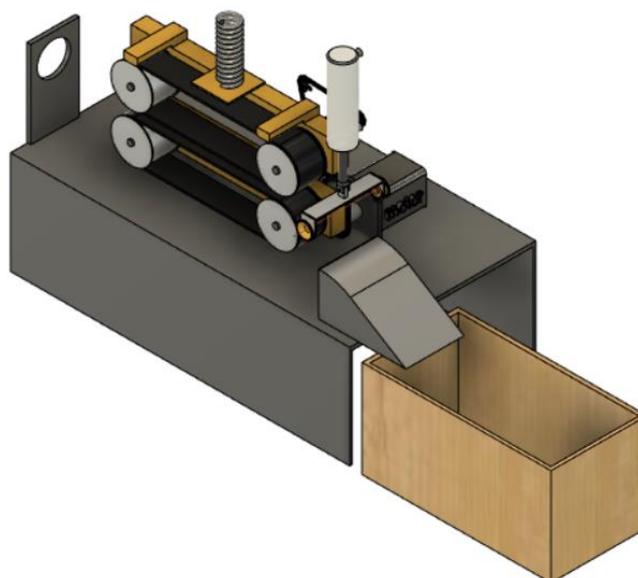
Vista frontal em perspectiva do conjunto das opções da máquina
